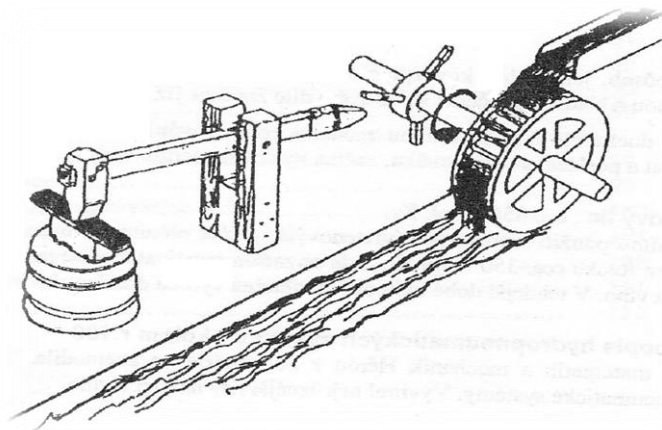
Různé druhy mechanizovaných kladiv [2]
